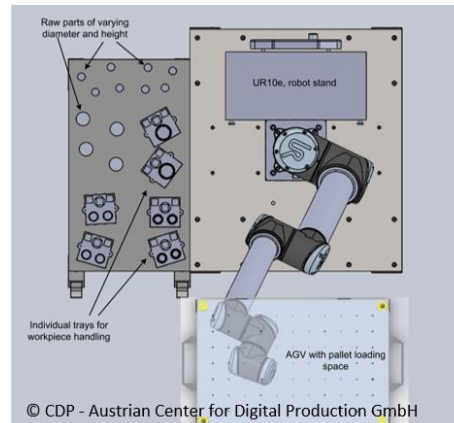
Beschreibung und Layout der *Adaptive Loading Station
